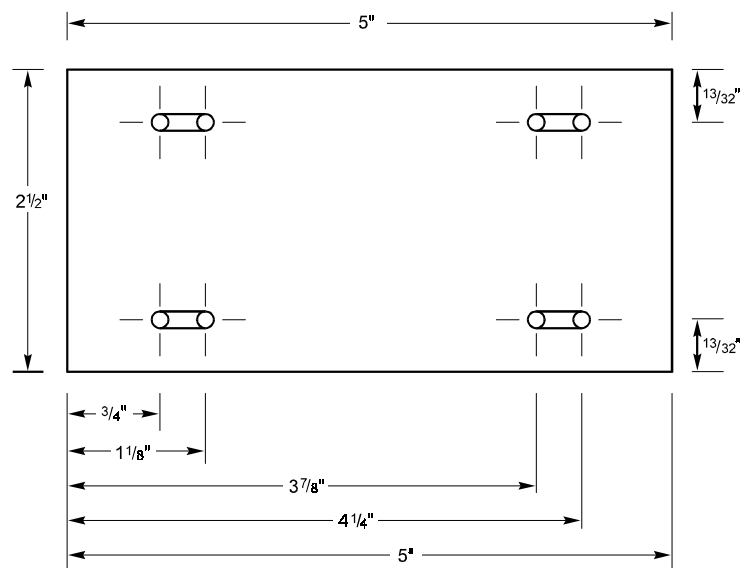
Размеры вспомогательной пластины для установки дисководов
